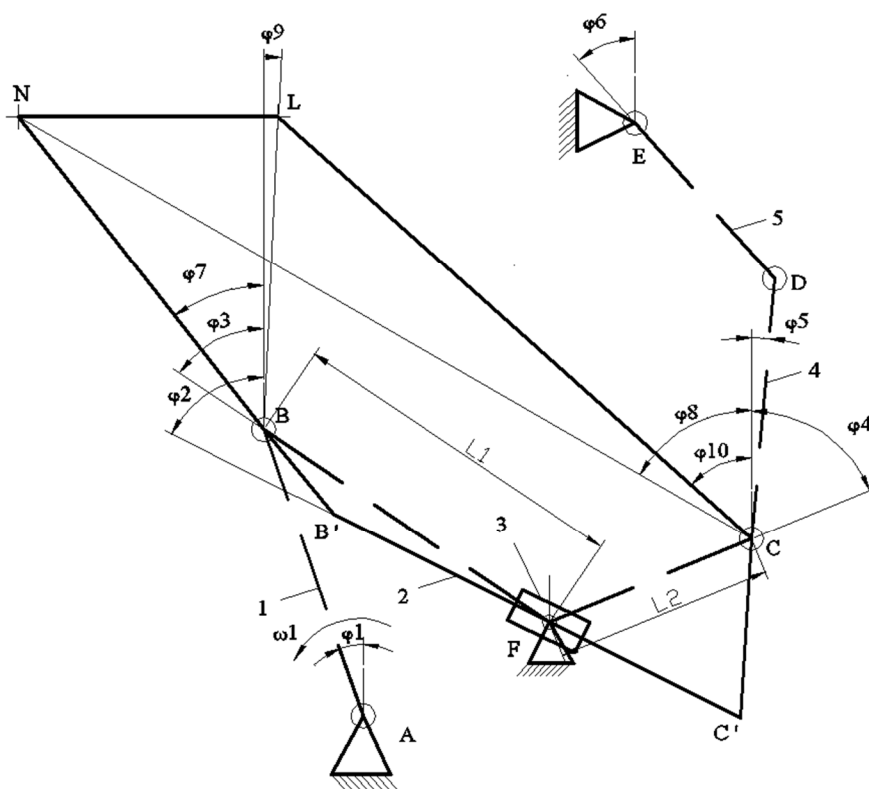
Схема плоского механизма, эквивалентного конструкции резцедержателя с регулируемым положением центра жесткости
